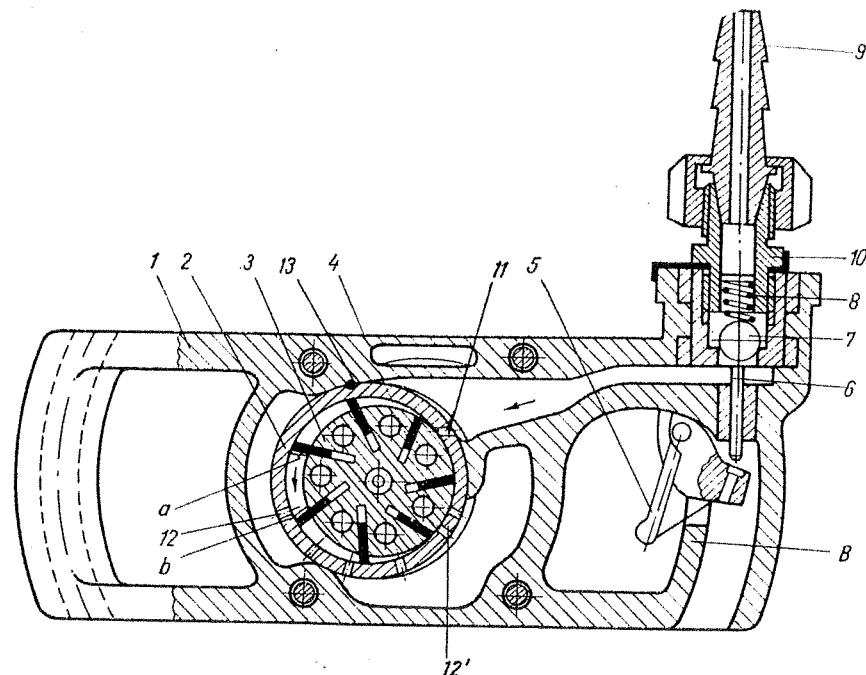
Secțiune prin perforatorul rotativ pneumatic PR-8.
